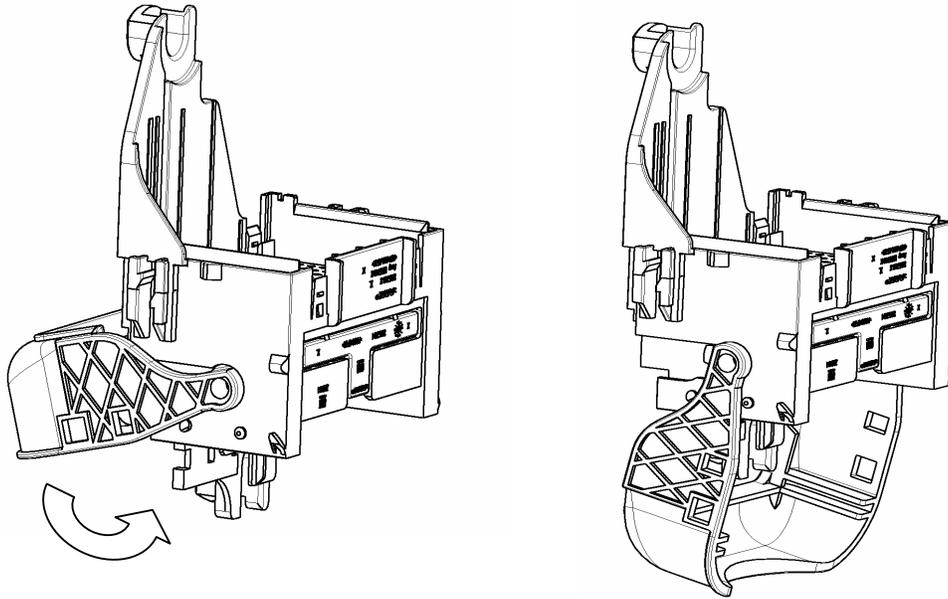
Hebel in die letzte Montageposition schwenken.
